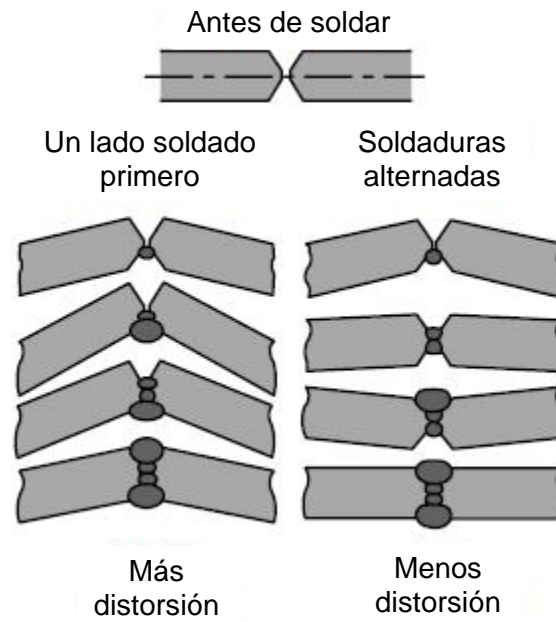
Reducción de distorsión angular usando doble junta en V alternando las soldaduras (6).
